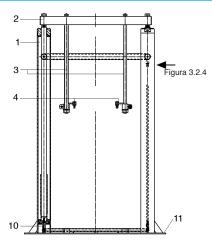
Elevador de dos columnas -Potencia de elevación: 0,75t, para bidón de 216,5 l
